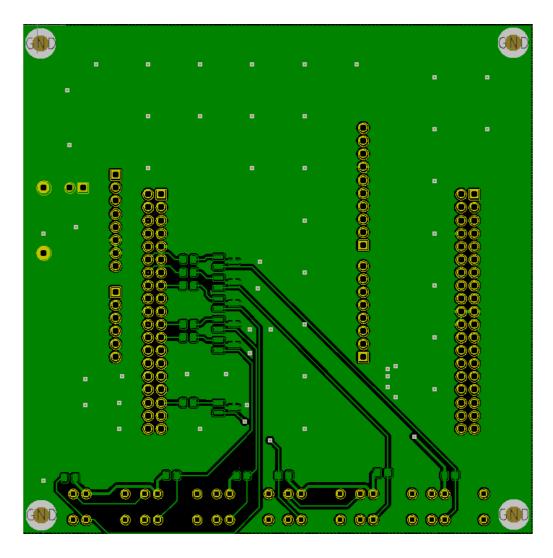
Schemat layoutu PCB łózka testowego dla wariantu 1.
